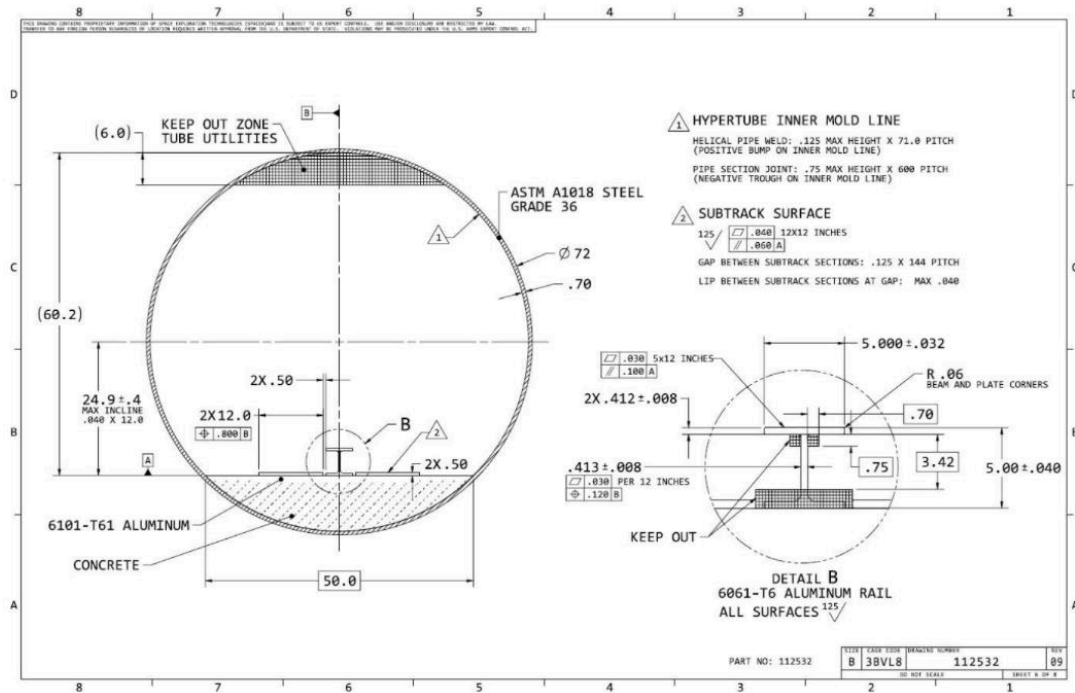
Plano del tubo de SpaceX con el raíl en su interior (Fuente: SpaceX)
